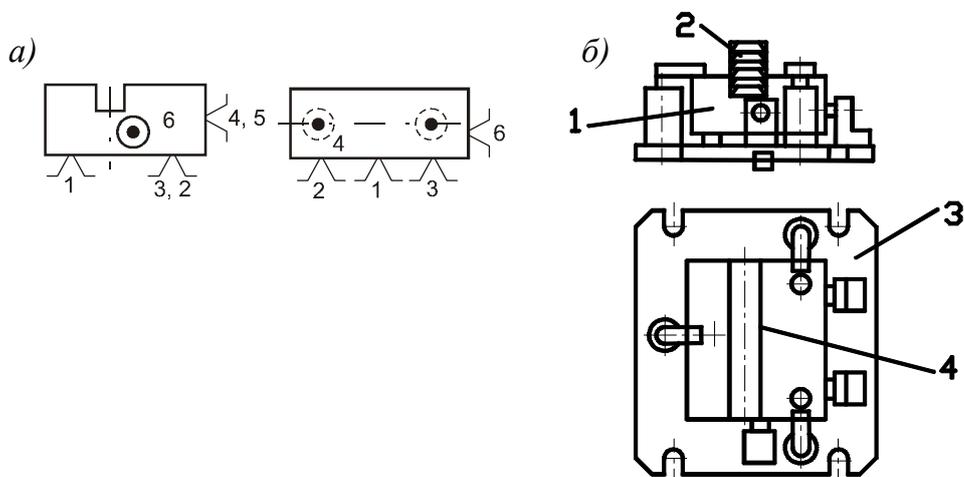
Схема базирования (*a*) и схема установки призматической заготовки в приспособлении при фрезеровании шпоночного паза (*б*): 1 – призматическая заготовка; 2 – дисковая фреза; 3 – приспособление; 4 – шпоночный паз в заготовке
